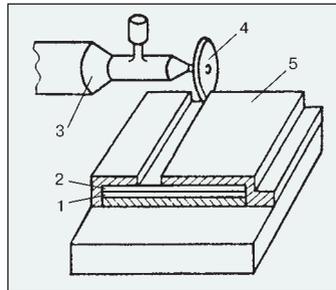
Схема роликовой СТ: 1, 2 — свариваемые заготовки; 3 — шпиндель; 4 — вращающийся ролик; 5 — прижимы
